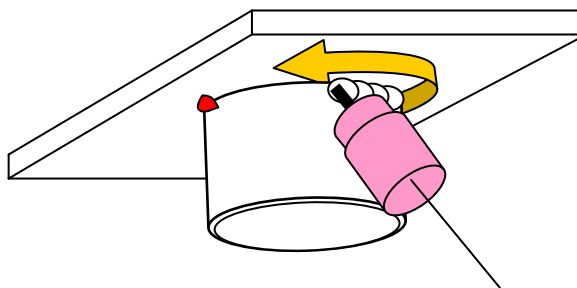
Posición del ensamble, para la realización de la soldadura sobre cabeza.
